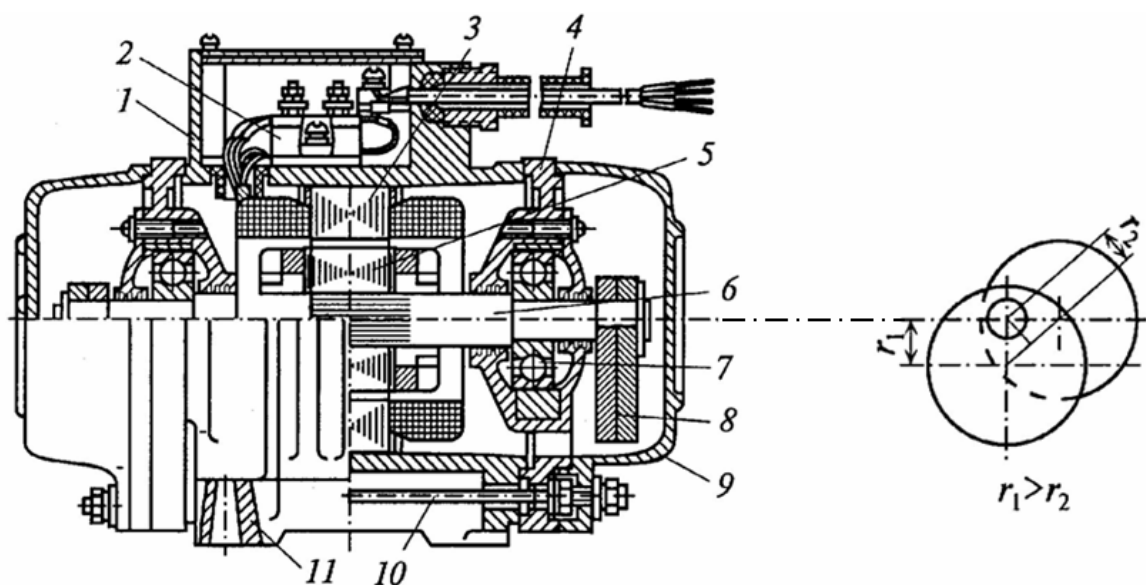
Электромеханический дебалансный одновальный вибратор ИВ-70 с круговыми колебаниями: а - общий вид; б - схема регулирования дебаланса; 1 - корпус; 2 - клеммная коробка; 3 - обмотка статора; 4 - щиты; 5 - ротор; 6 - вал; 7 - подшипник; 8 - дебалансы; 9 - крышки; 10 - шпильки; 11 - установочные лапы
